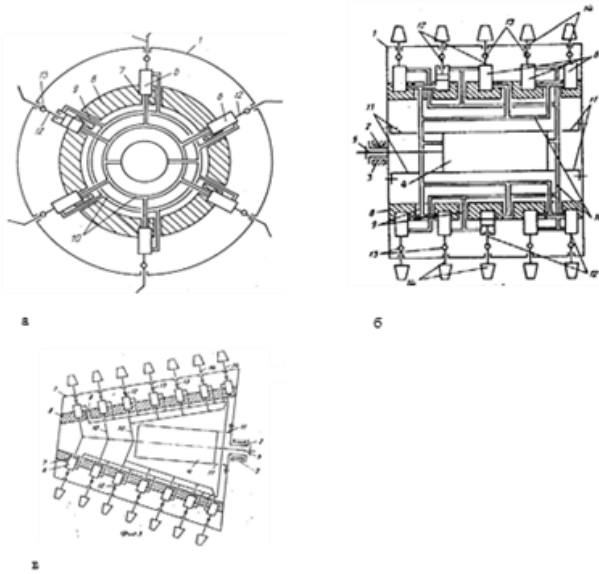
Исполнительный орган: а – продольный разрез; б – поперечный разрез; в – продольный разрез исполнительного органа конической формы; 1 – корпус; 2 – полый приводной вал; 3 – стрела; 4 – гидронасос; 5 – приводной вал; 6 – гидровибраторы; 7 – радиальные гнёзда; 8 – барабан; 9 – окна; 10 – гидромагистраль; 11 – кронштейны; 12 – штоки; 13 – шарниры; 14 – режущий инструмент
